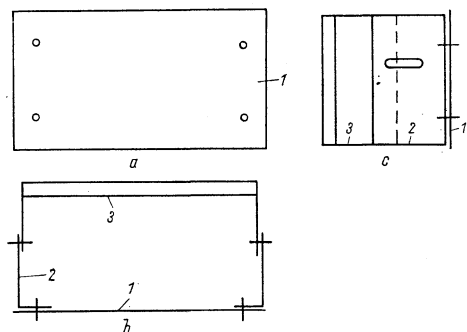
Frontplatte und Chassis für die Flachbauweise; 1 — Frontplatte, 2 — Blechwinkel, 3 — Chassis; a — Vorderansicht, b — Draufsicht, c — Seitenansicht
